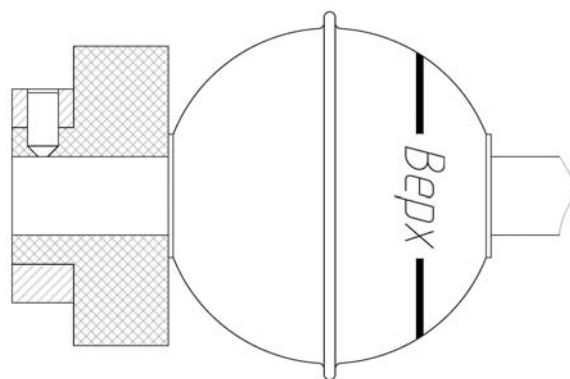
Установка фиксатора под срез торца измерительного элемента
